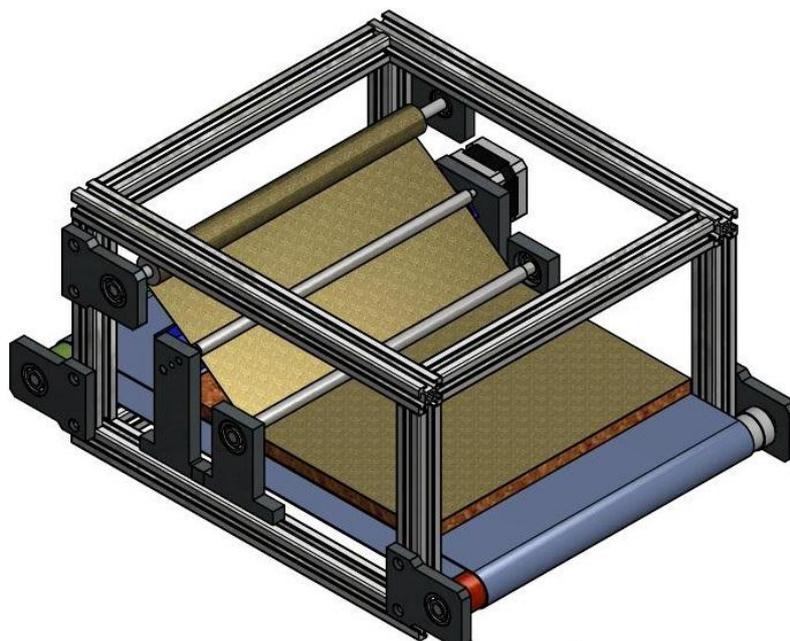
3D-модель устройства для нанесения ламинации
